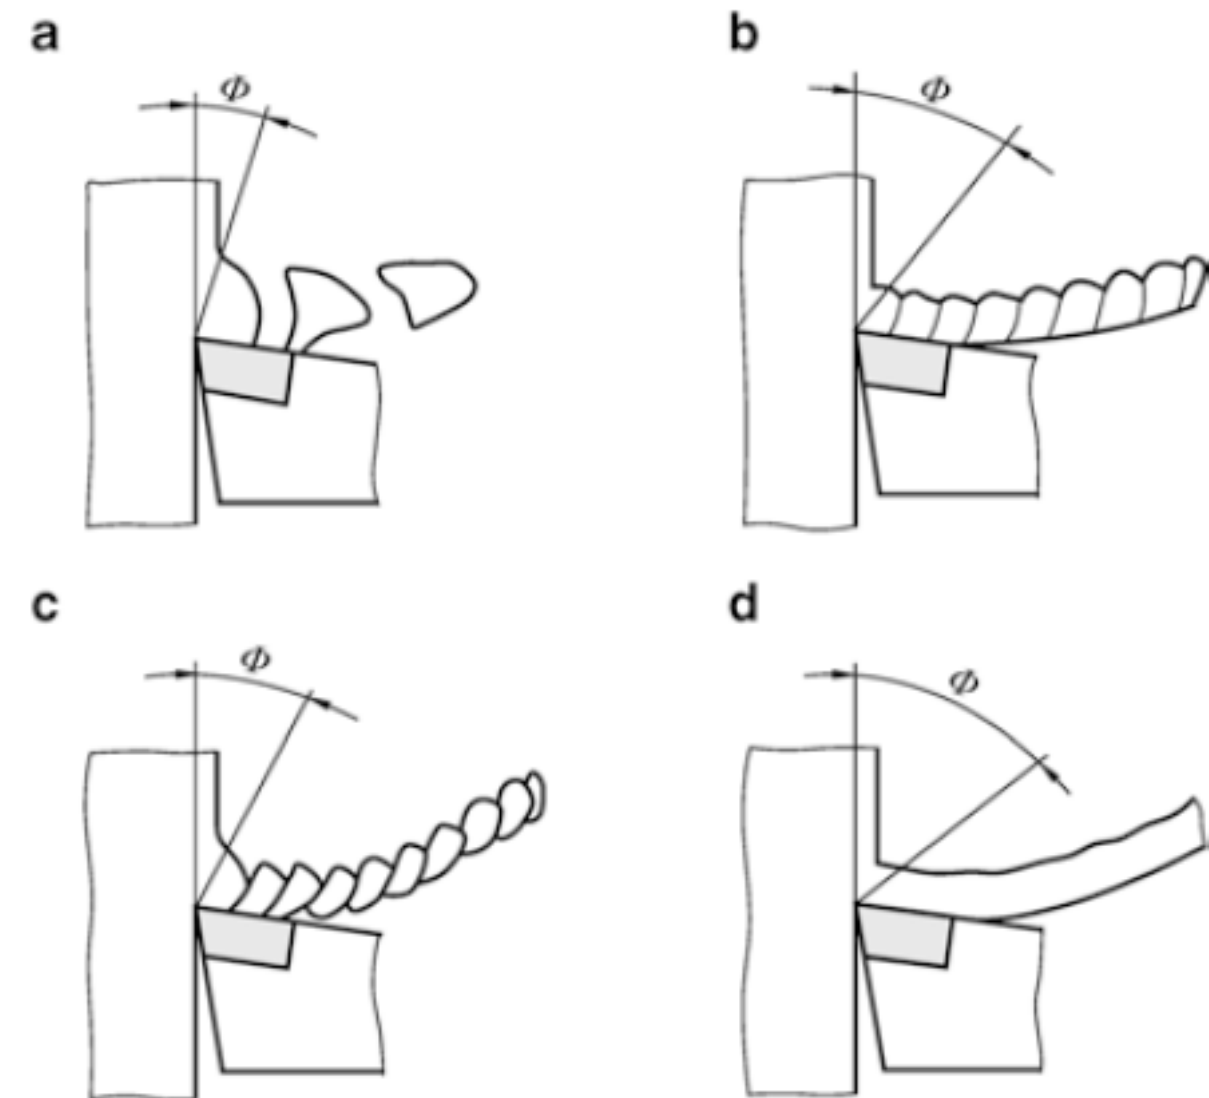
Spanarten: a Reißspan, b Scherspan, c Lamellenspan, d Fließspan
